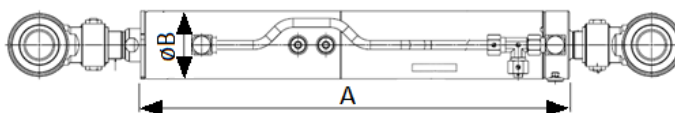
Rozměry hydromotoru pro přední nápravu
